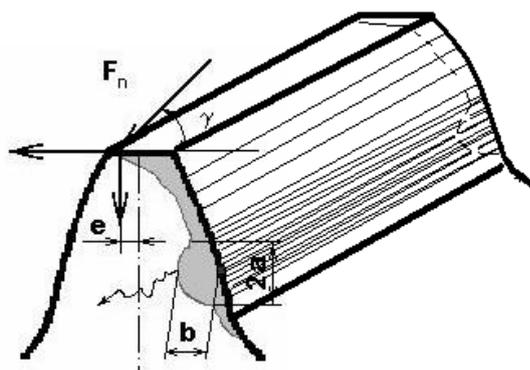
Эпюра износа зуба шестерни зубчатой передачи
